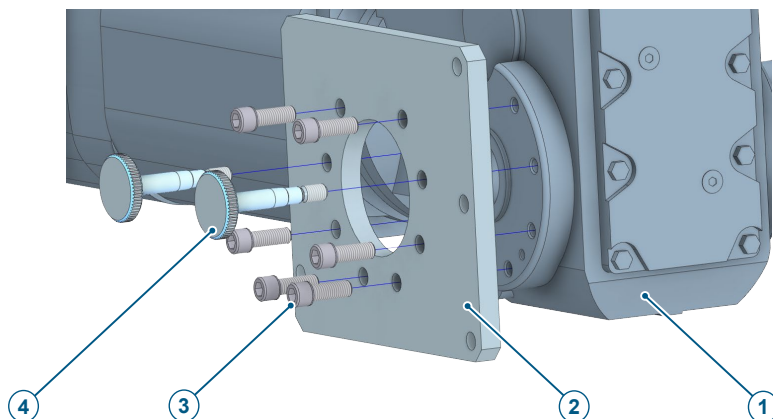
Montaje de la placa de brida en el accionamiento completo
